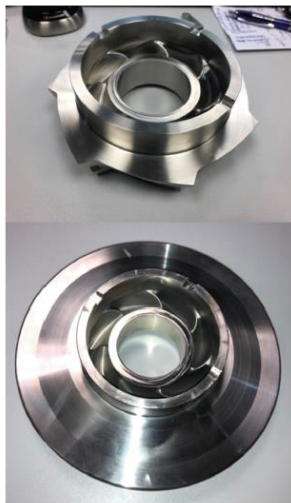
Рабочее колесо, изготовленное процессом лазерного осаждения металлов с механической обработкой.
